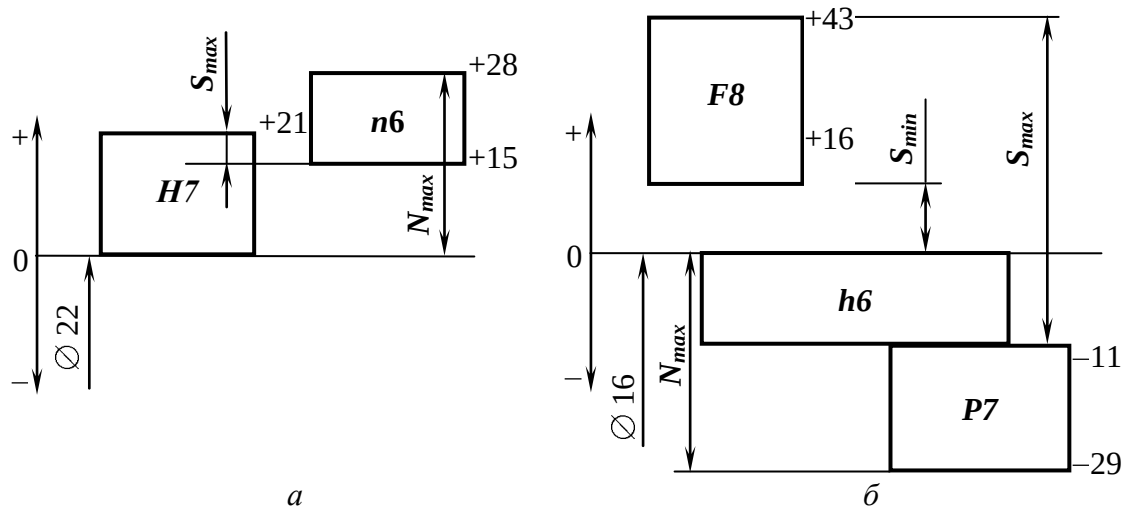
Схемы полей допусков посадок в соединениях:
